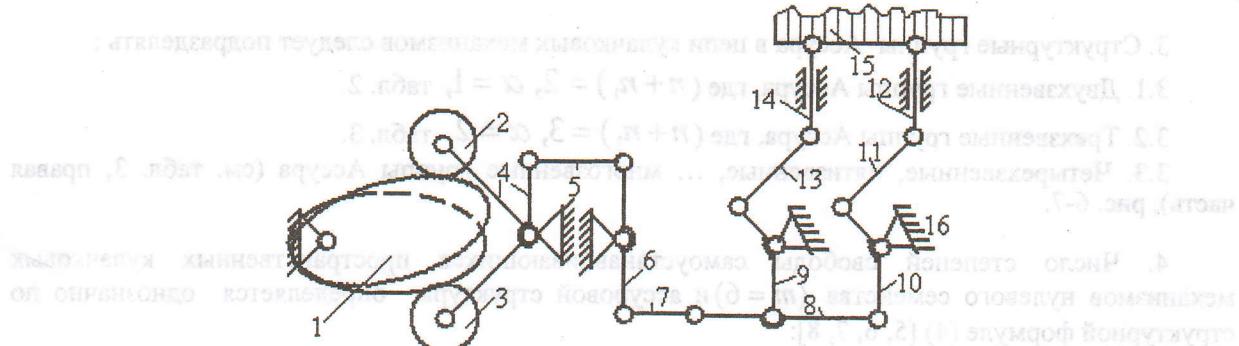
Шестнадцатизвенный самоустанавливающийся механизм для возвратно-поступательного перемещения ремизок ткацкого станка.
